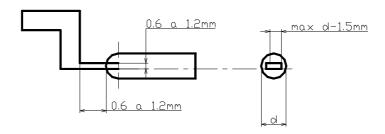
Dimensionado del canal de estrangulamiento.
